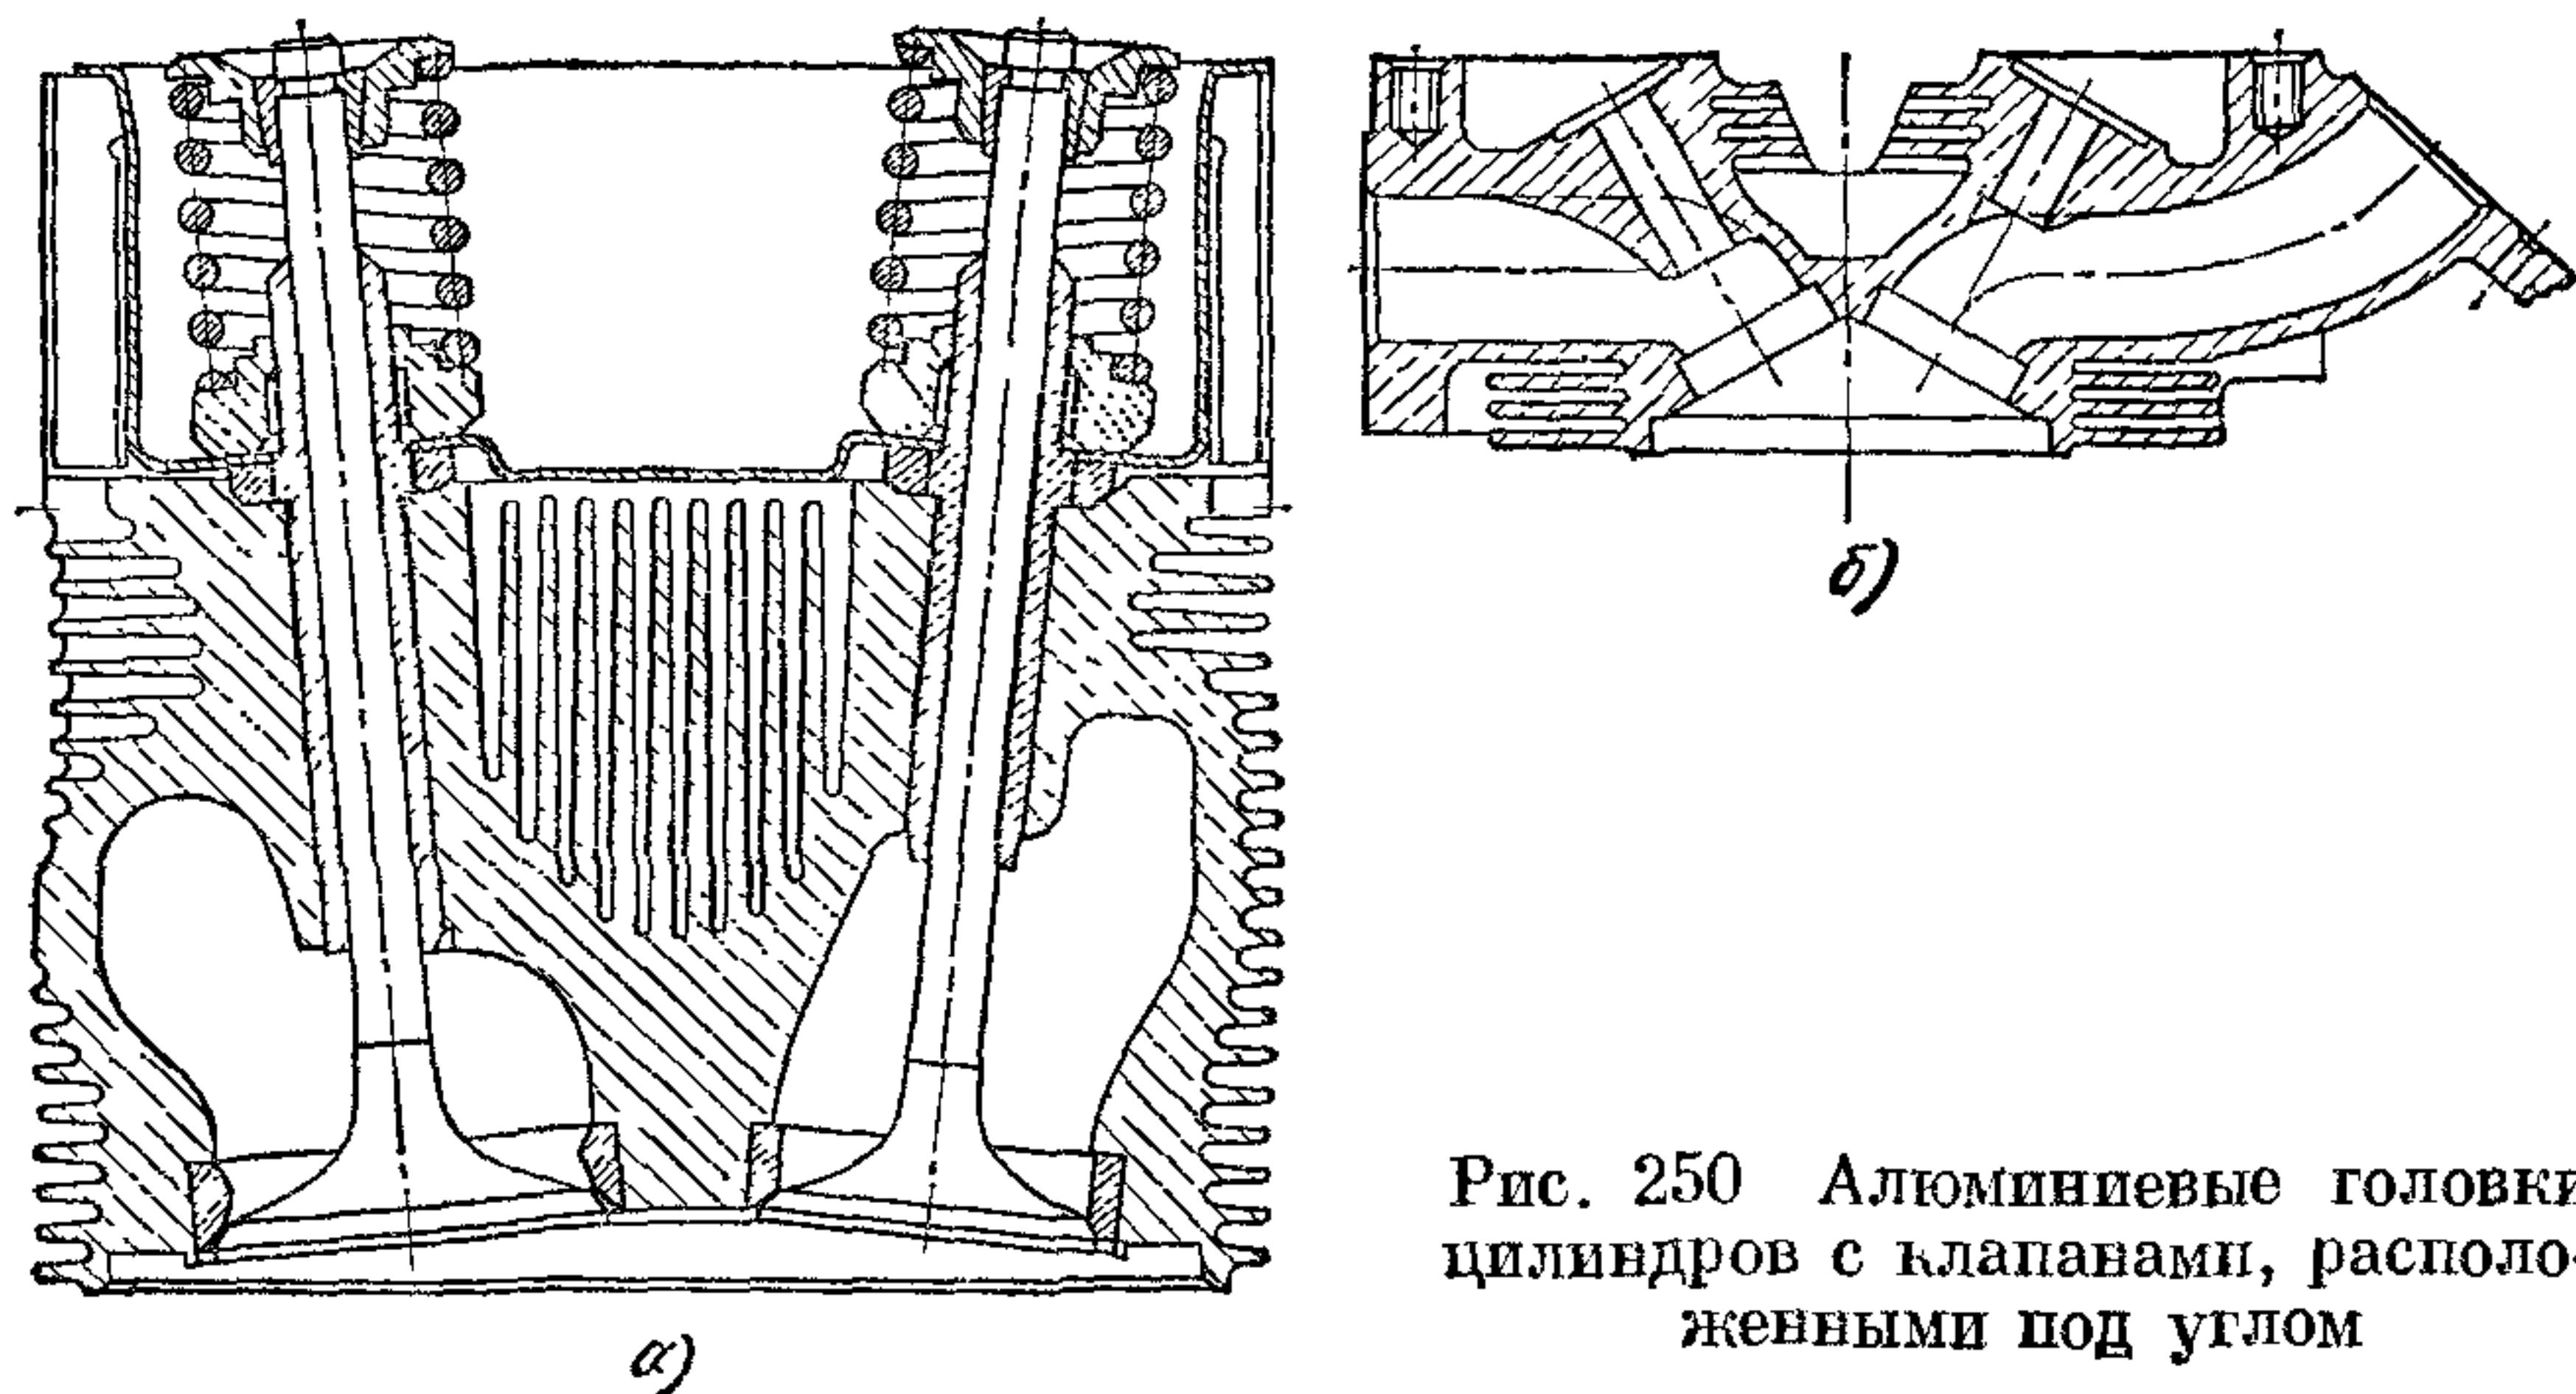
Алюминиевые головки цилиндров с клапанами, расположенными под углом
